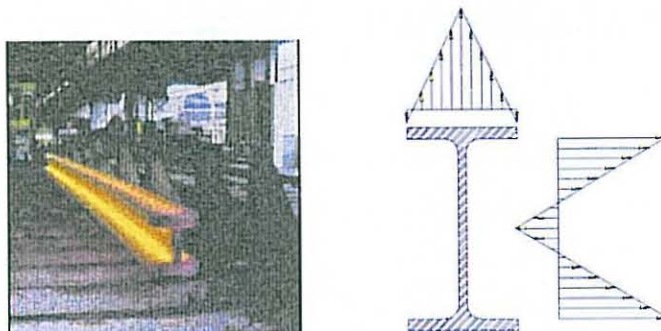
Arrefecimento não uniforme das vigas metálicas laminadas a quente.
